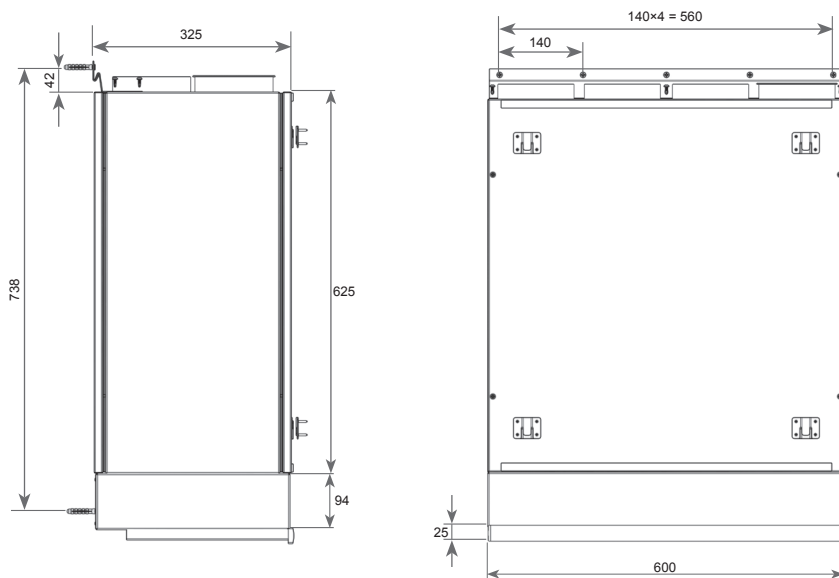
Instalace standardní kuchyňské digestoře
